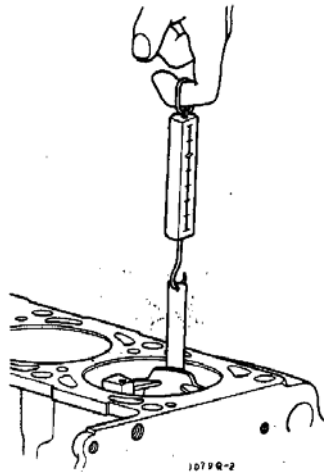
Подбор поршня к цилиндрам двигателя
